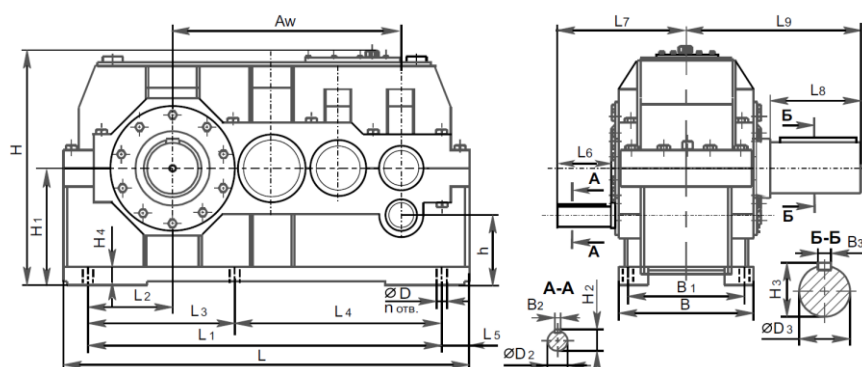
Конструктивная схема редуктора 7Ц4-1035
